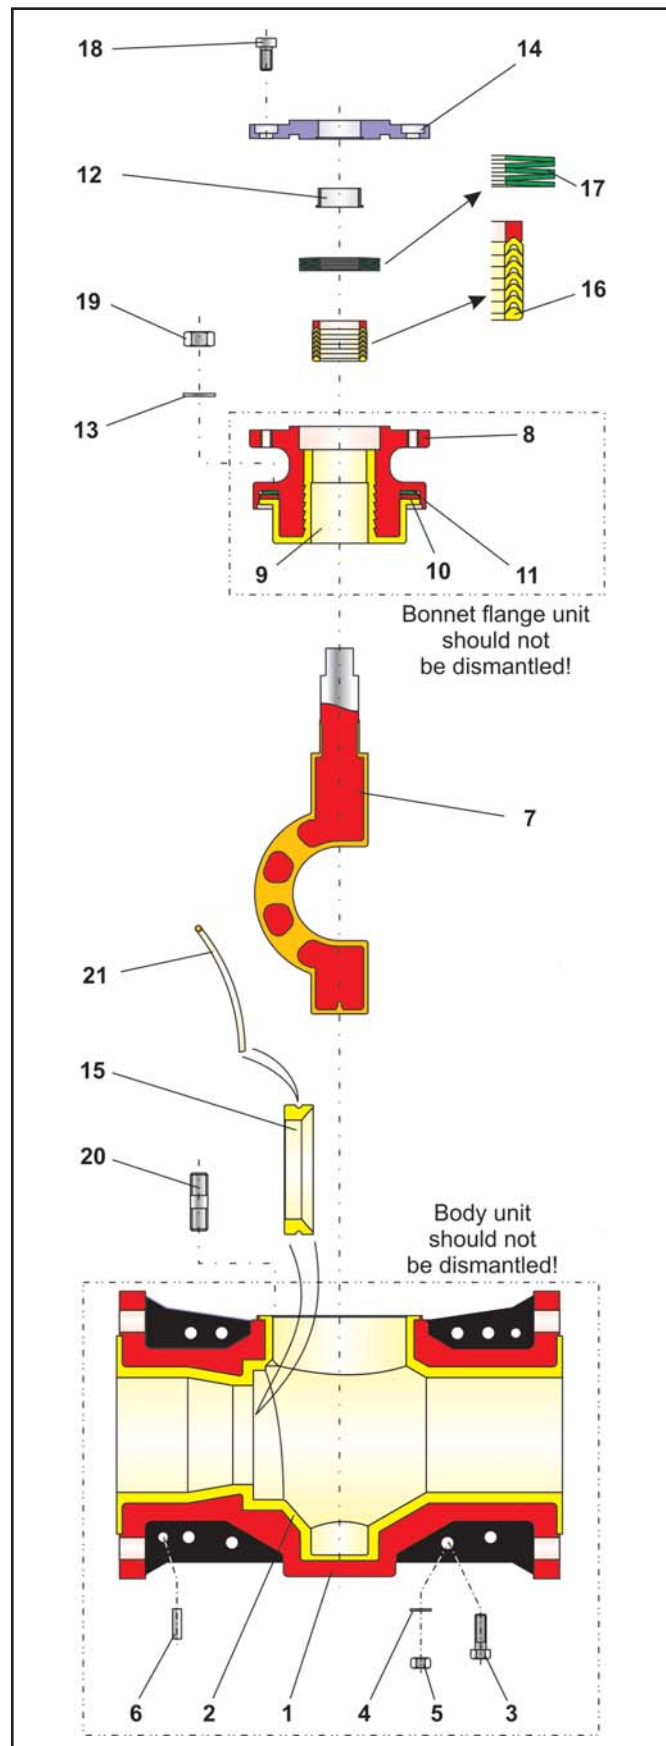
Explosionszeichnung des Drehkegelventils BR 23e
